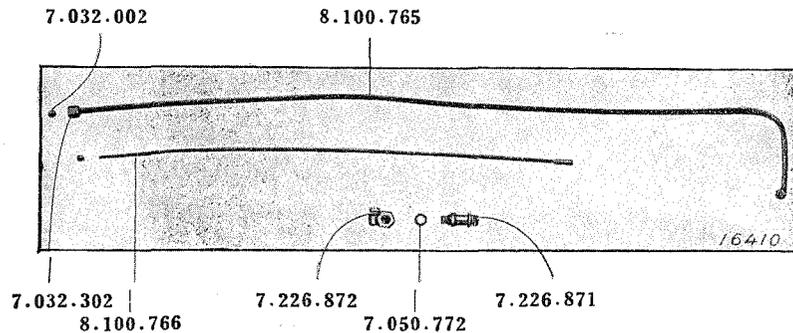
Graissage de la butée de débrayage et du cardan.
